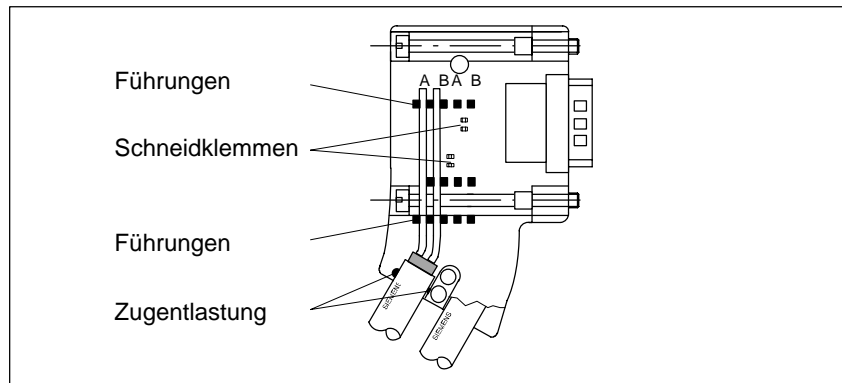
Buskabel am Busanschlußstecker (6ES7 972-0BA30-0XA0) anschließen
